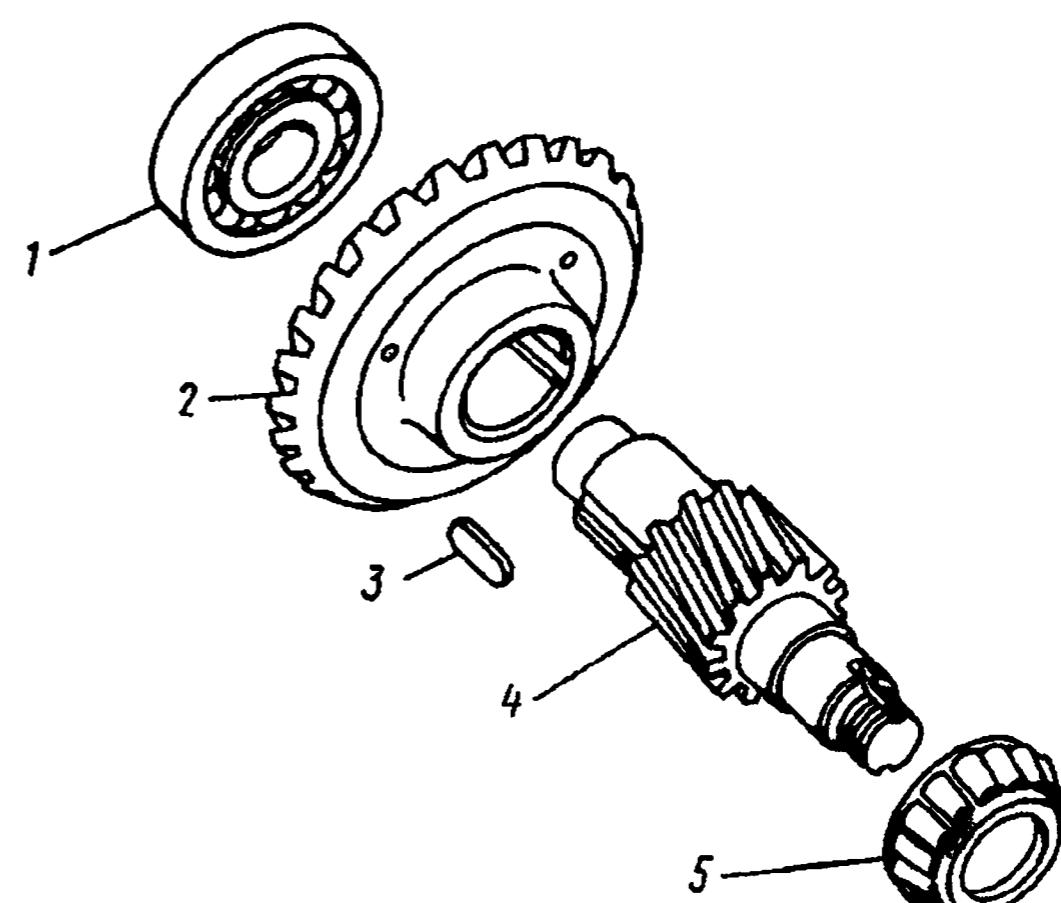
Узел ведущего цилиндрического зубчатого колеса в сборе:
